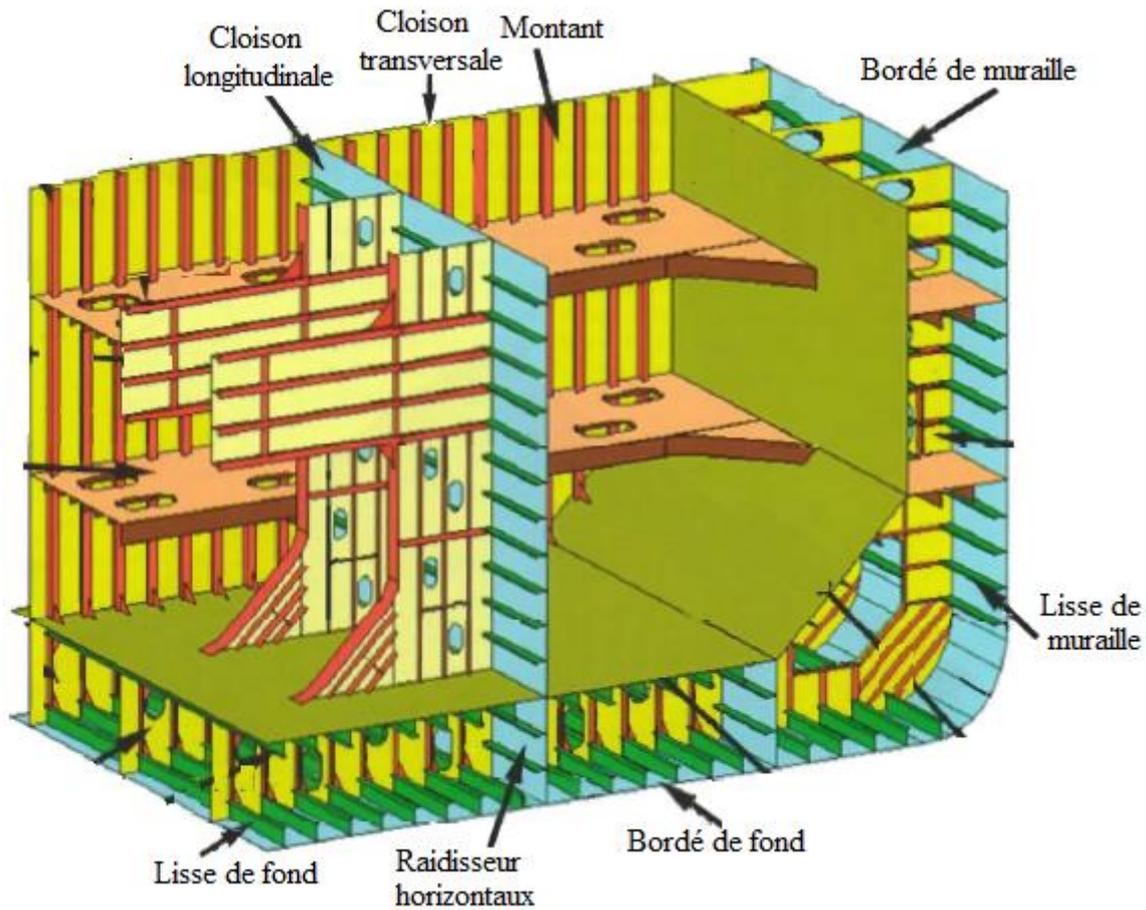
Construction de la cloison transversale et longitudinale dans la structure du navire.
